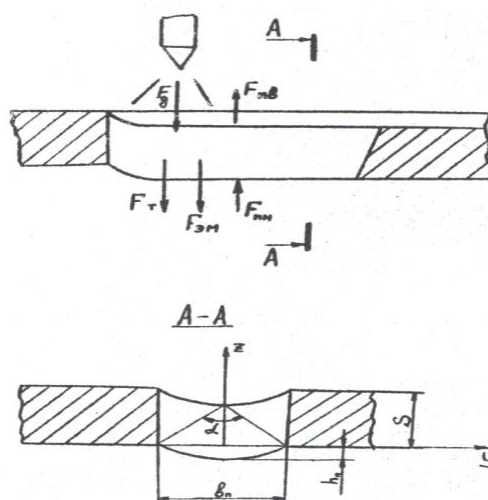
Равновесие сварочной ванны [Equilibrium of the weld pool]
